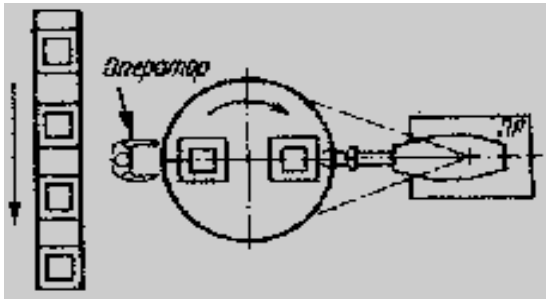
Схема сварочного комплекса с поворотным столом
